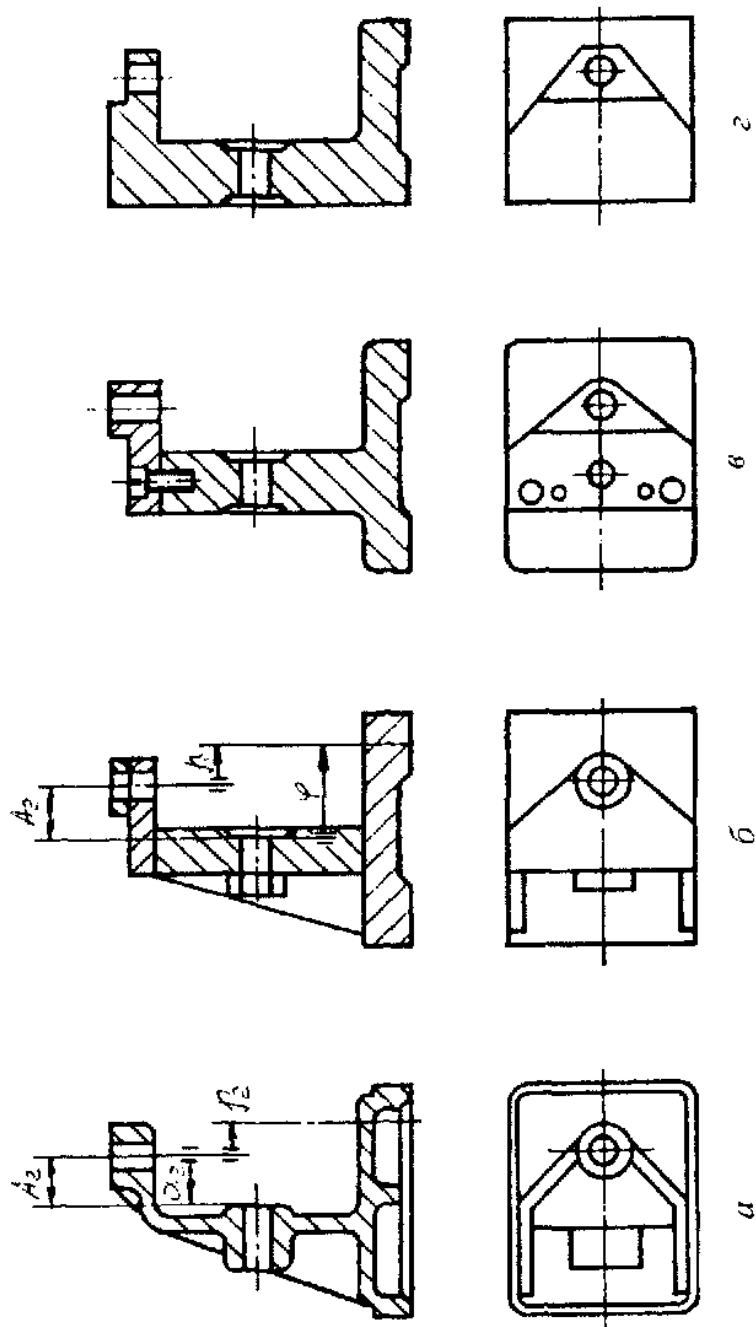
Варіанти виготовлення корпусу кондуктора: *a* – виливаного; *б* – зварюваного; *в* – збірного; *г* – каваного (після зняття напусків та припусків)
